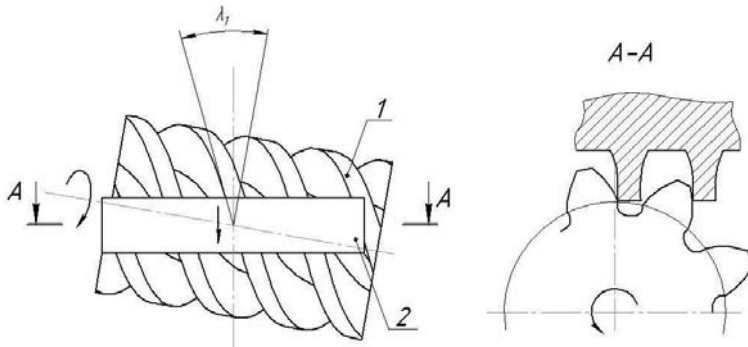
Схема работы инструмента червячного типа со сплошными винтовыми режущими кромками
